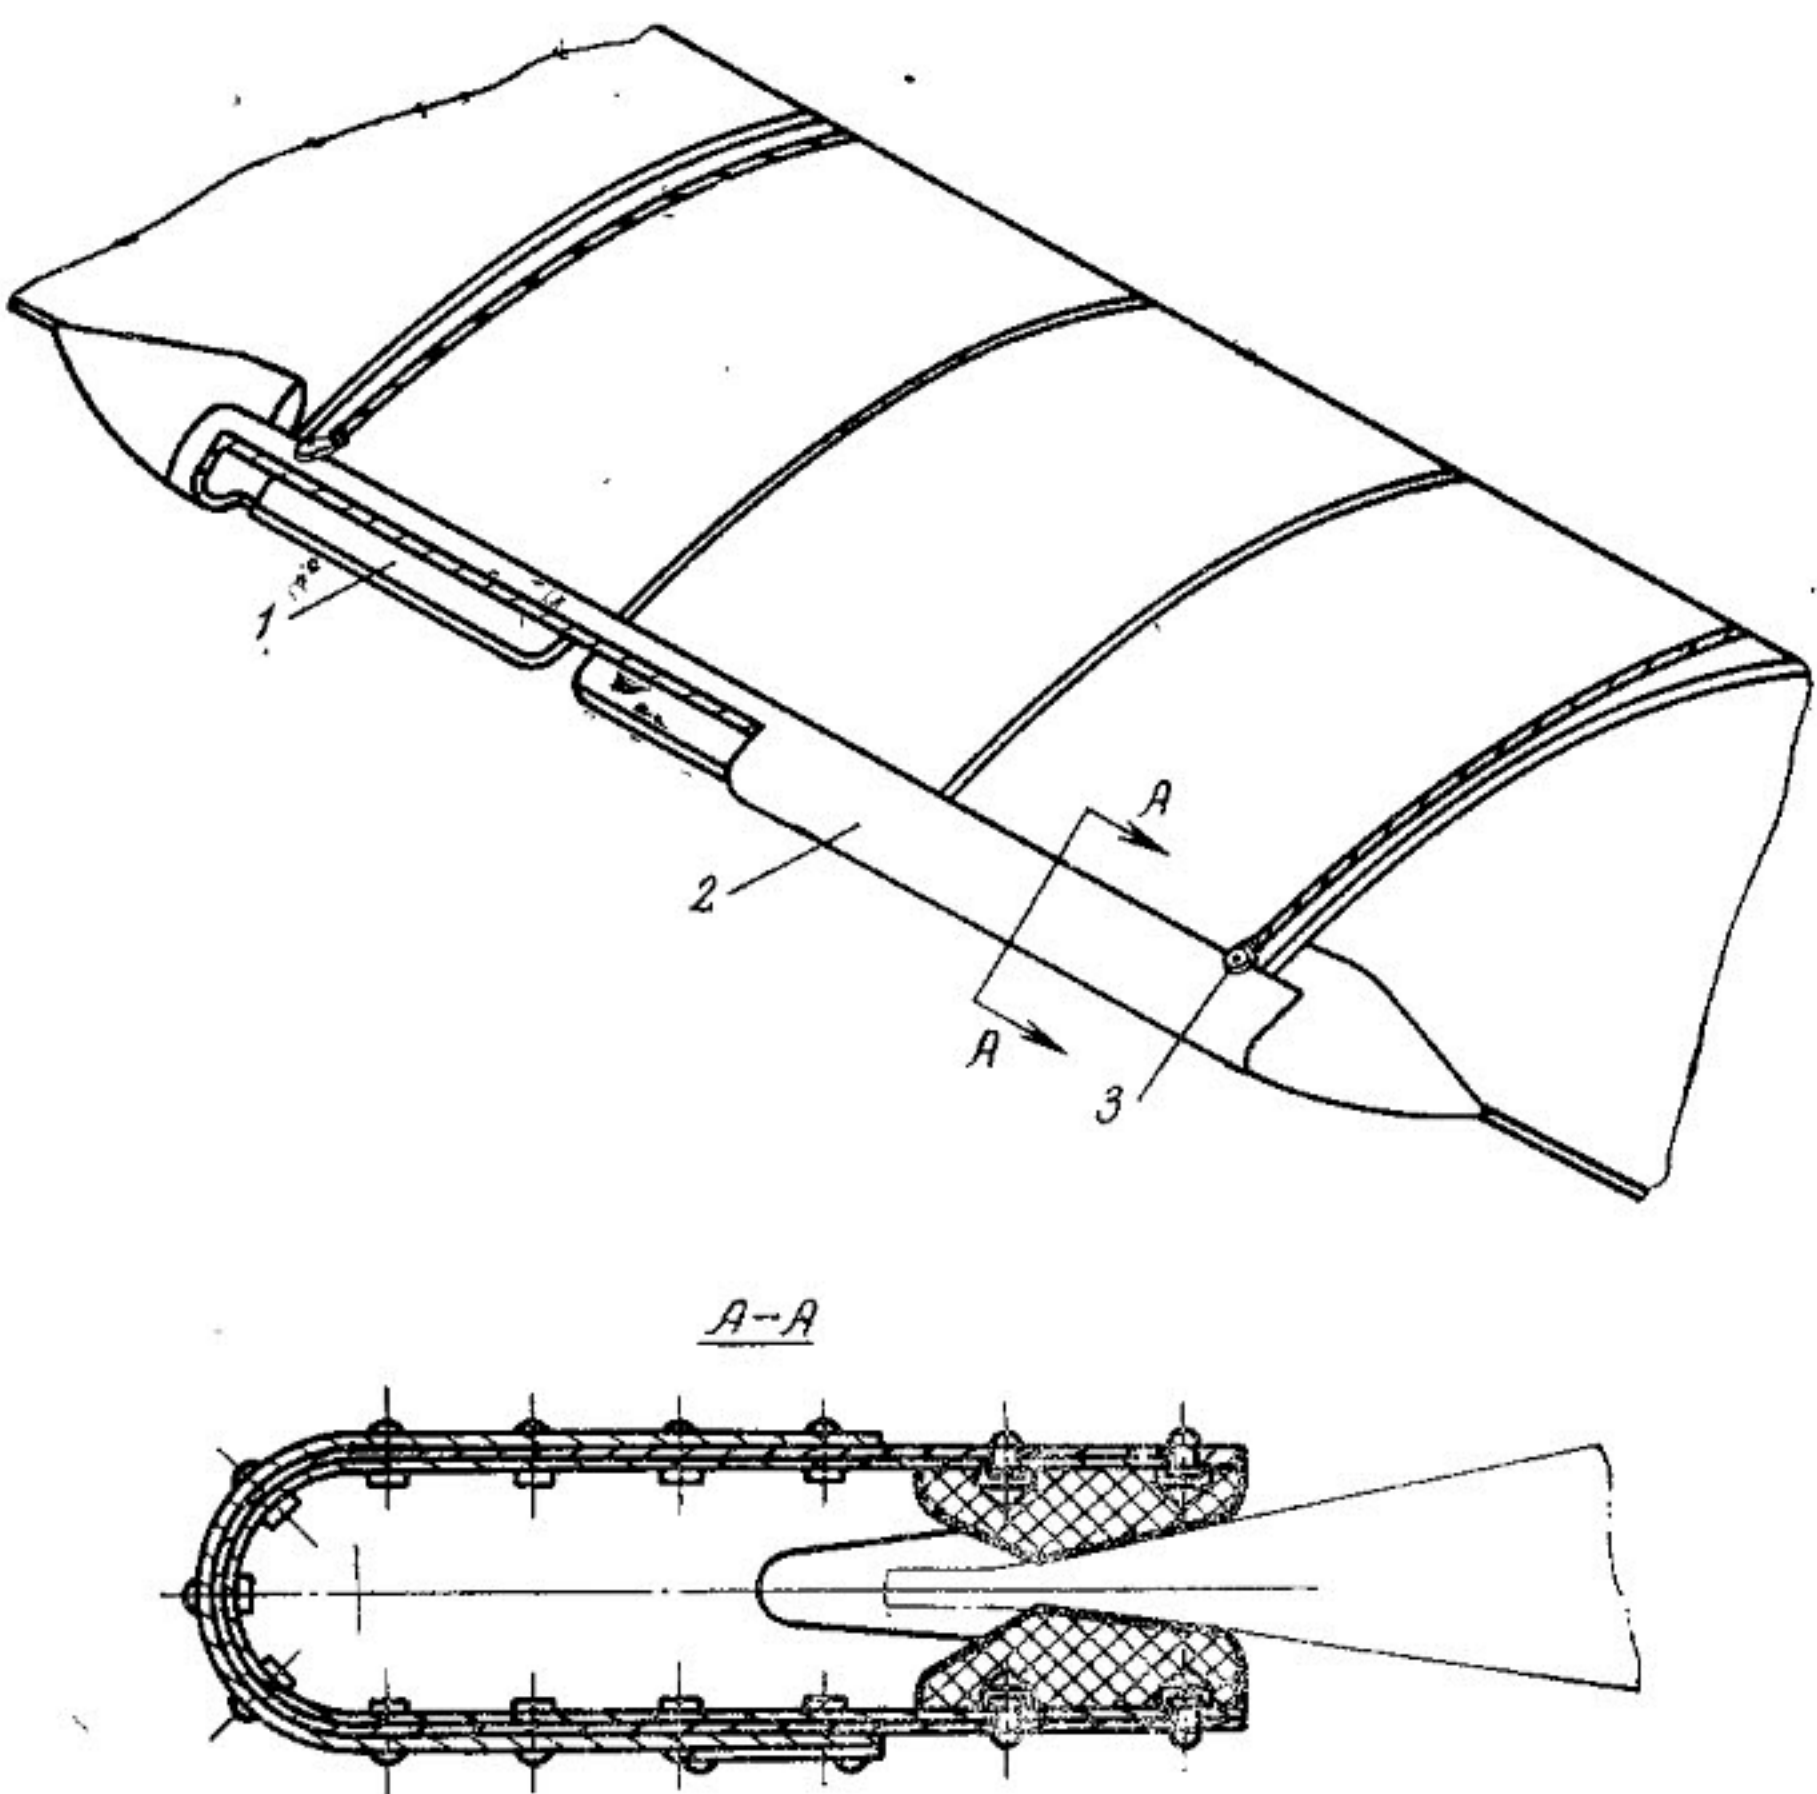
Предохранитель закрывков лопастей несущего винта: 1—закрывок; 2—кожух; 3—амортизатор
